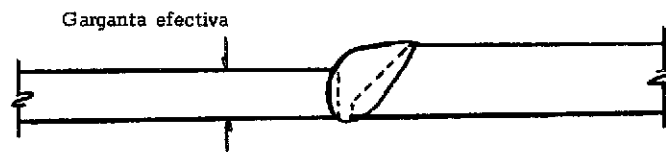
Soldadura de bisel de penetración completa.
